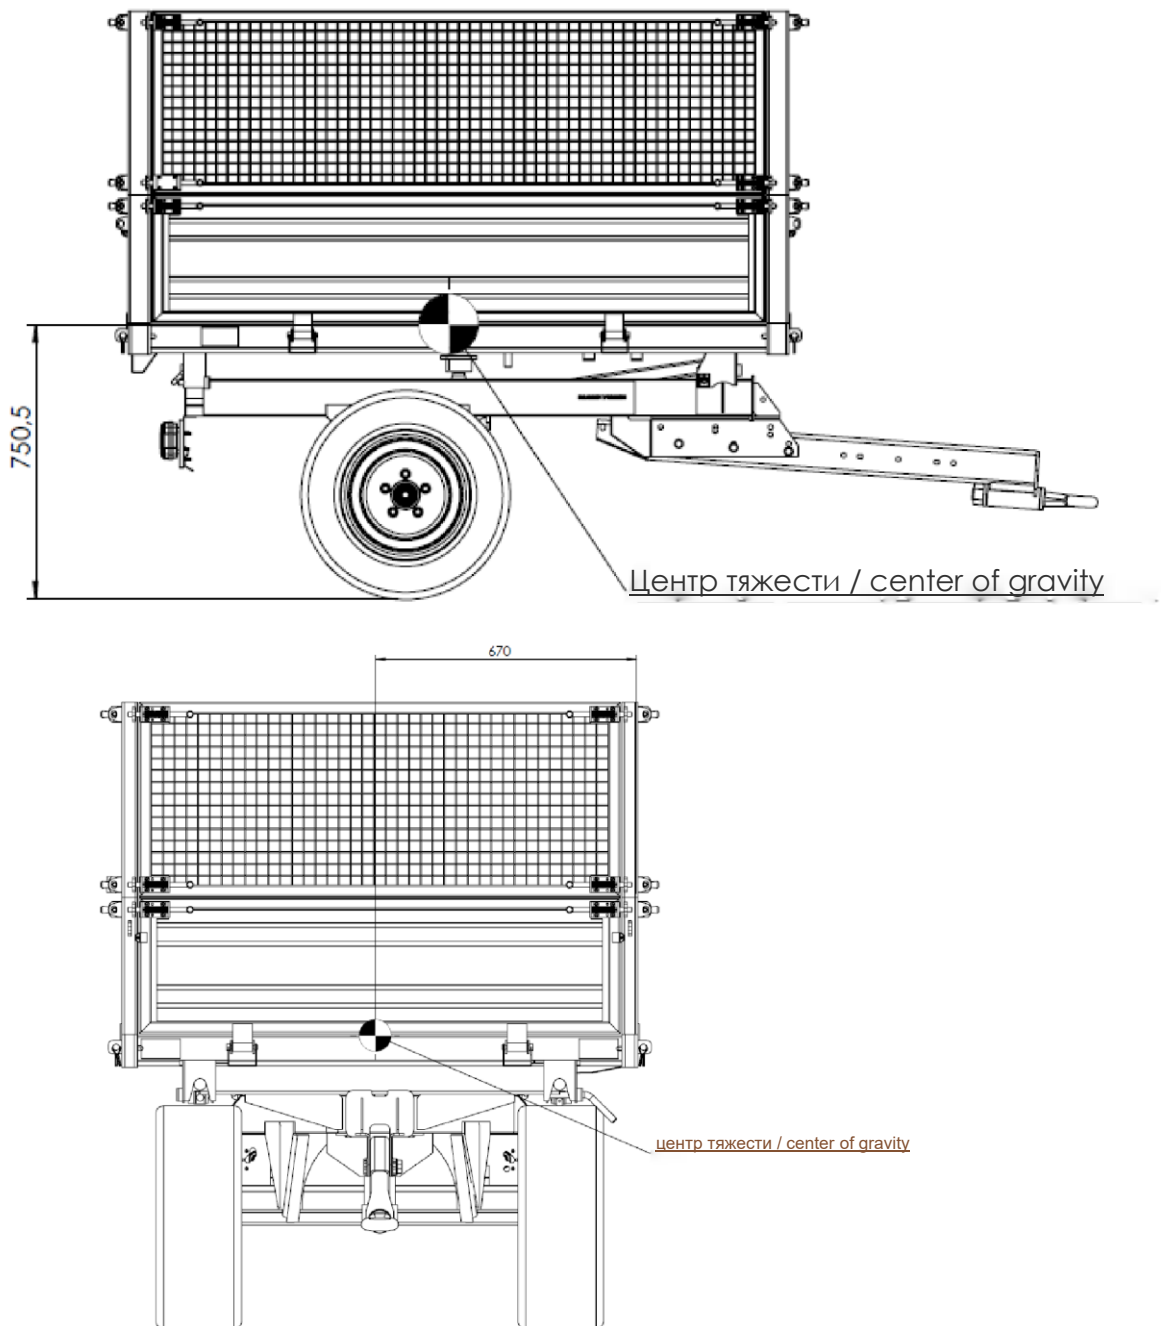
Размеры прицепа Т963/3 - вид сбоку
